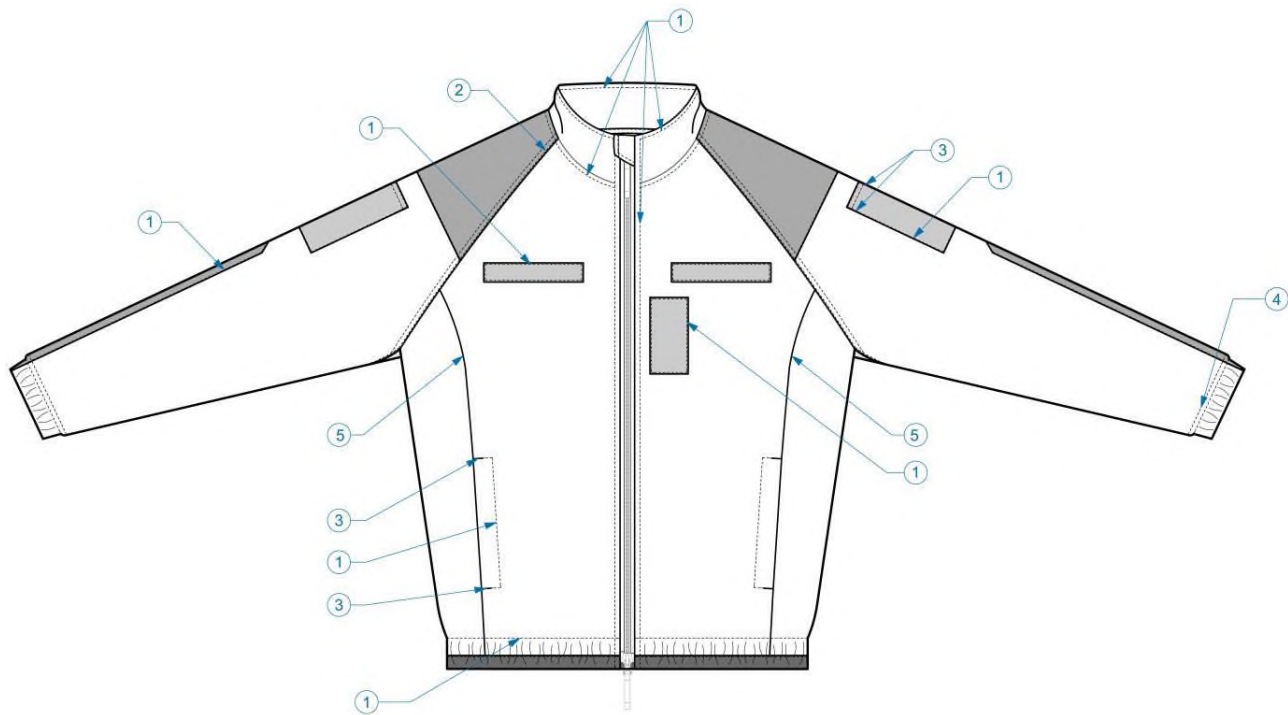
Строчки предмета (вид спереду)/
